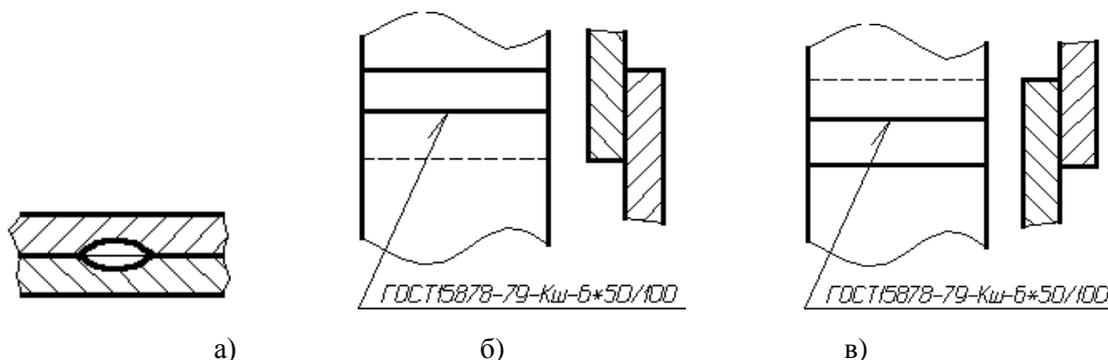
Шов соединения внахлестку прерывистый: а) форма поперечного сечения шва; б) с лицевой стороны; в) с оборотной стороны
